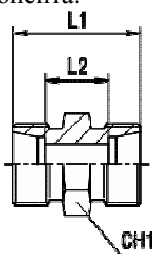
Чертеж прямого резьбового адаптера – соединителя.
